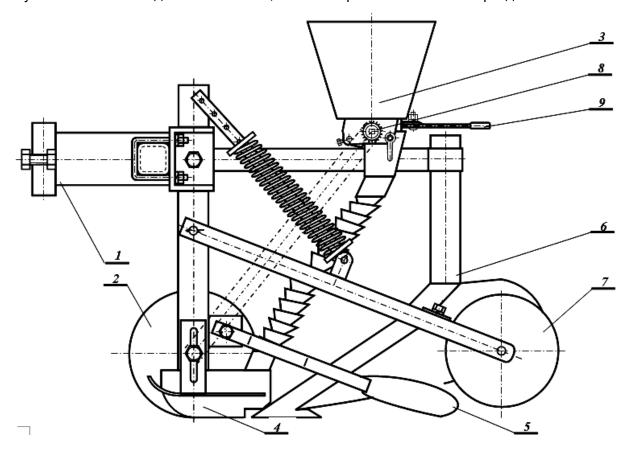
Конструктивная схема комбинированной малогабаритной двухрядной сеялки ТЗК-2:
